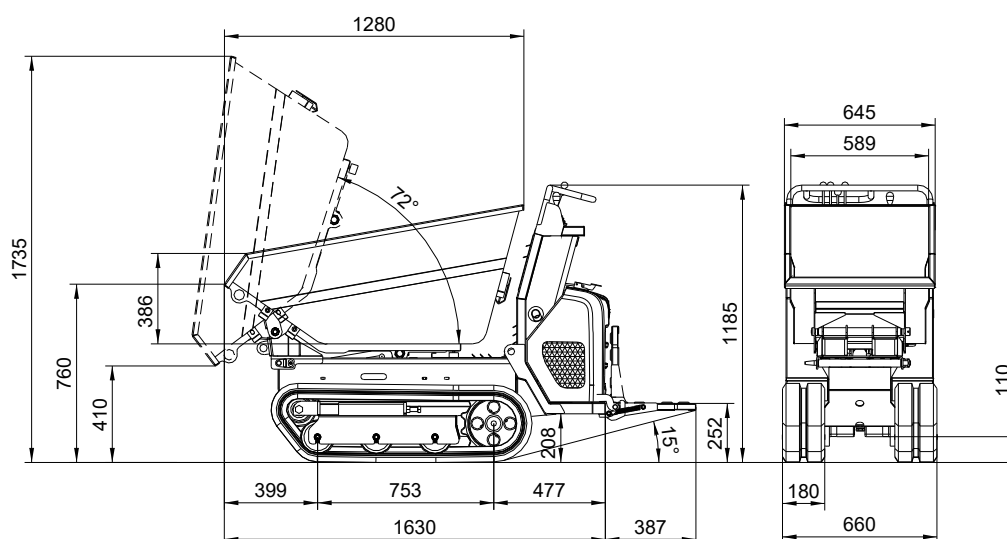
Dimensions de la machine (modèle DT05-P avec benne)
